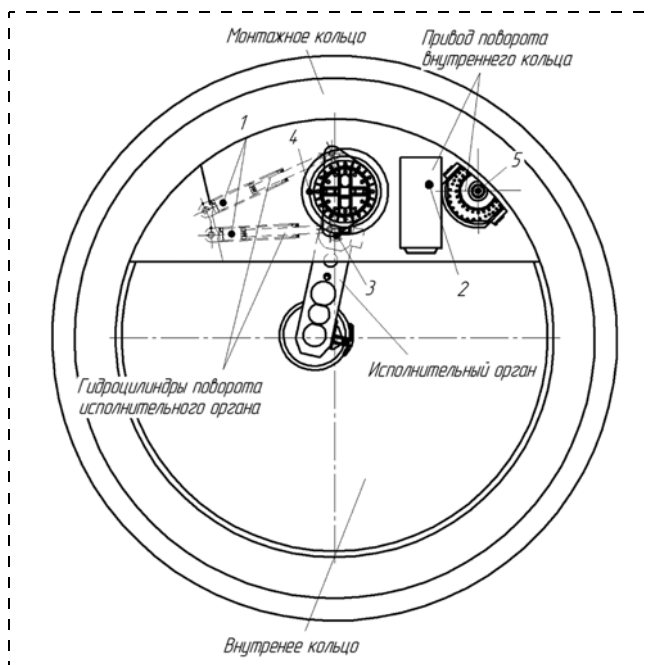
Схема расположения измерительной аппаратуры: 1 — датчики давления гидроцилиндров поворота исполнительного органа; 2 — датчики давления привода поворота внутреннего кольца; 3 — амперметр привода шнековой фрезы исполнительного органа; 4 — энкодер поворота исполнительного органа; 5 — энкодер поворота внутреннего кольца
